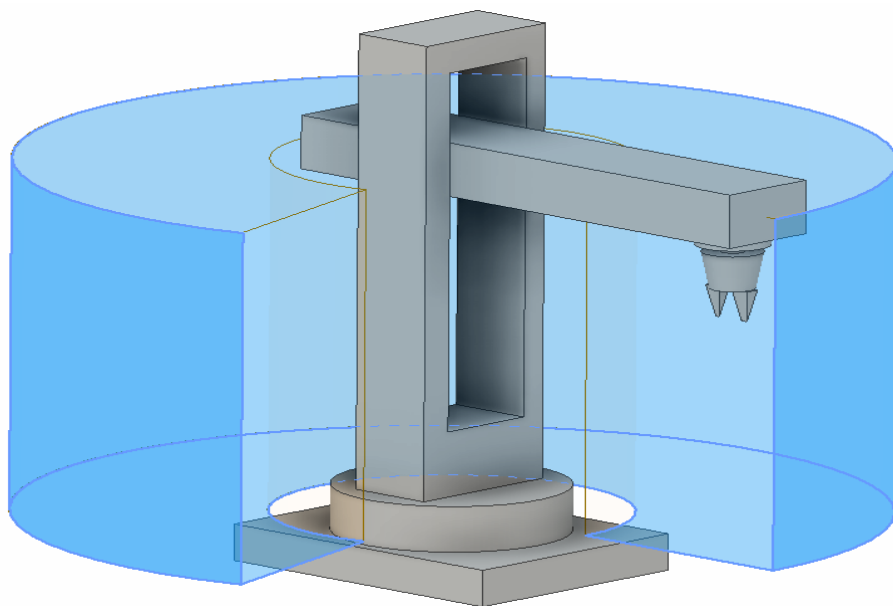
Циліндричний тип маніпулятора з виділеною робочою зоною
